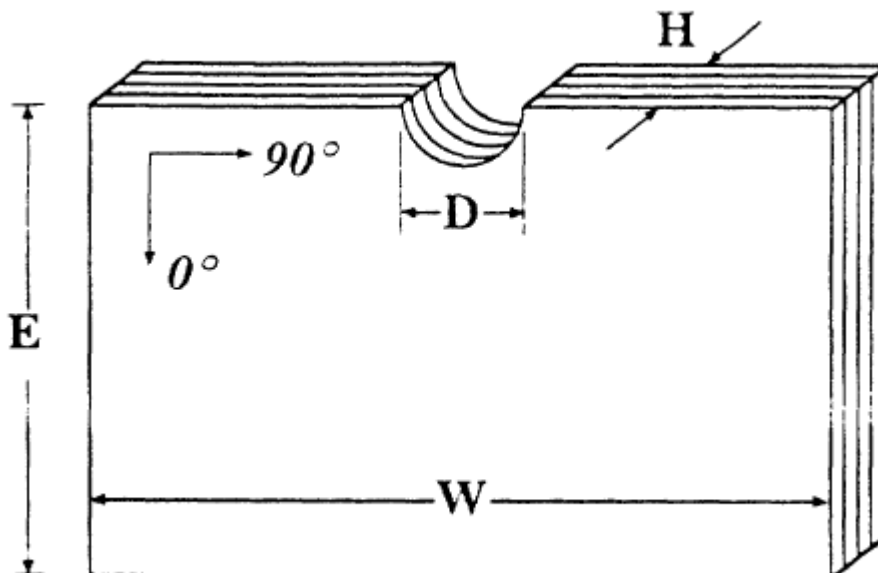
Forma e dimensões dos provetes a utilizar no ensaio *Pin-Bearing*. [34]
